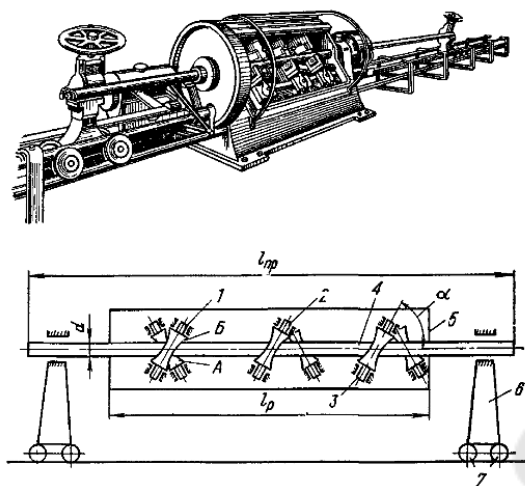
Общий вид (а) и схема (б) правильного станка
